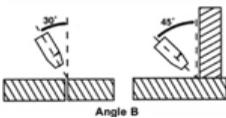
Положение сопла горелки при сварке, угол В
